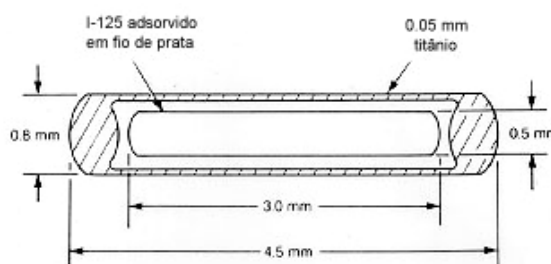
Desenho esquemático da semente a ser produzida pelo IPEN.
